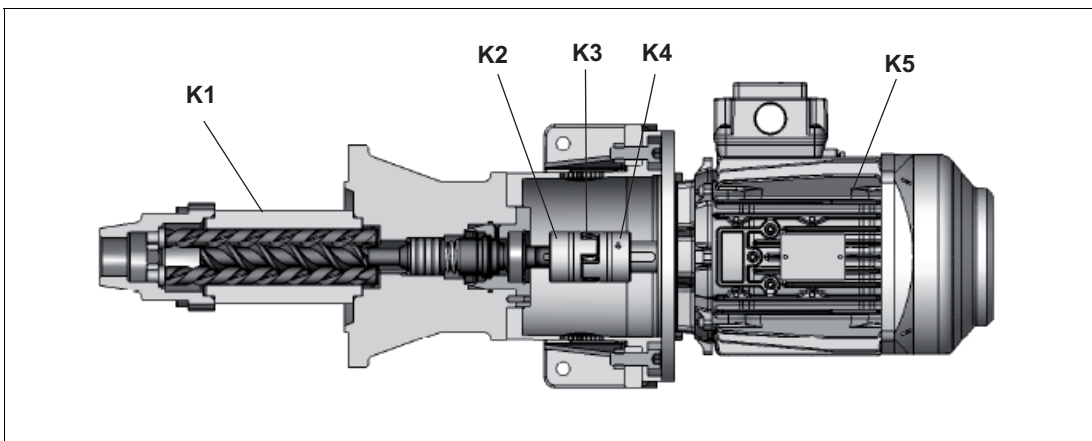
Estructura de la bomba de husillo roscado con acoplamiento y motor
